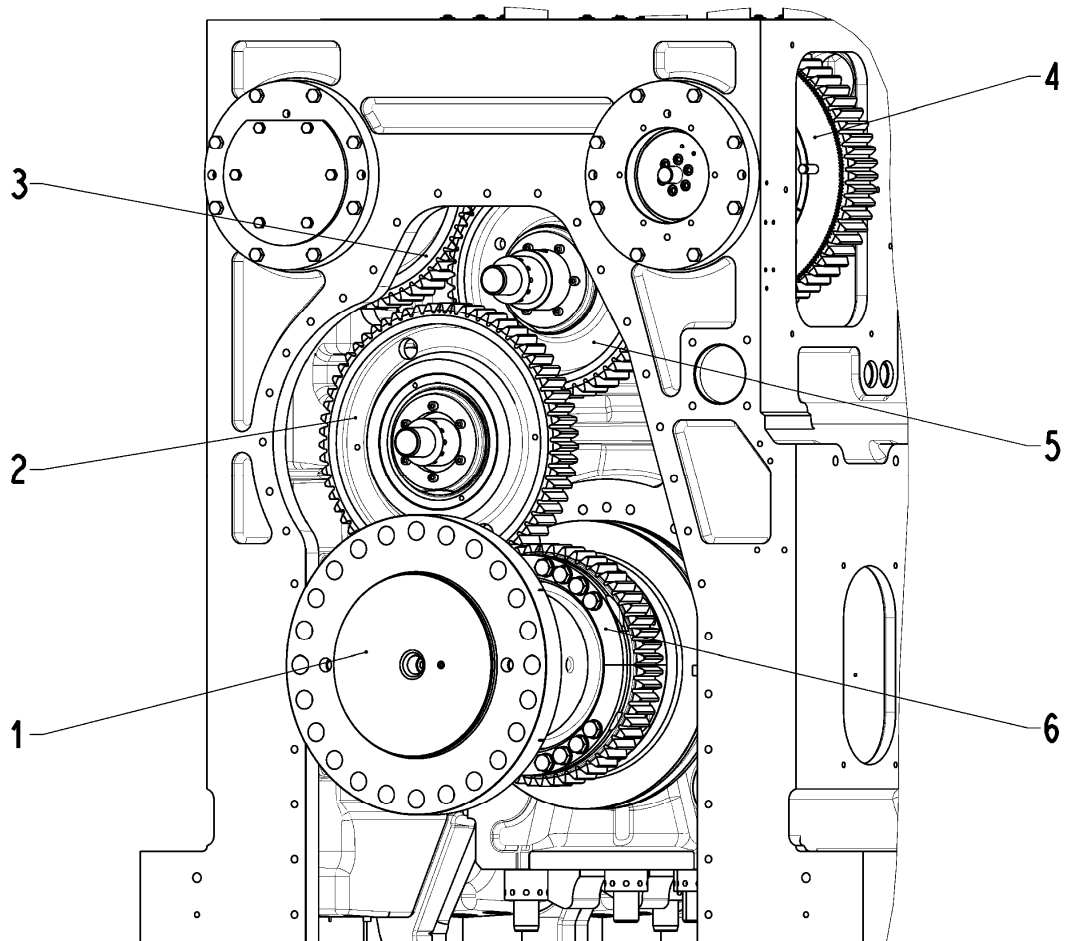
Привод розподільчого валу: 1 – фланець; 2, 5 – проміжна шестерня; 3 – шестерня приводу розподільчого валу; 4 – шестерня приводу валу ПНВТ
